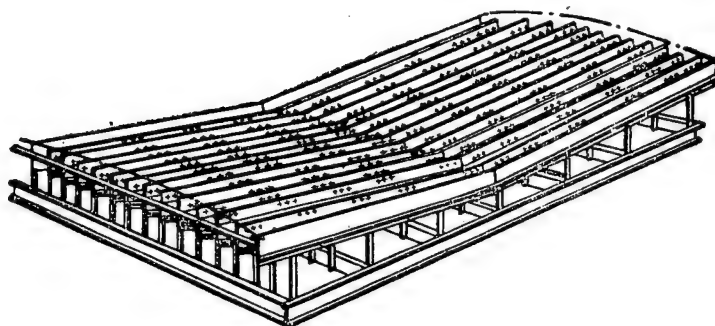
Постель с переставными лекалами для сборки и сварки секций палубы
